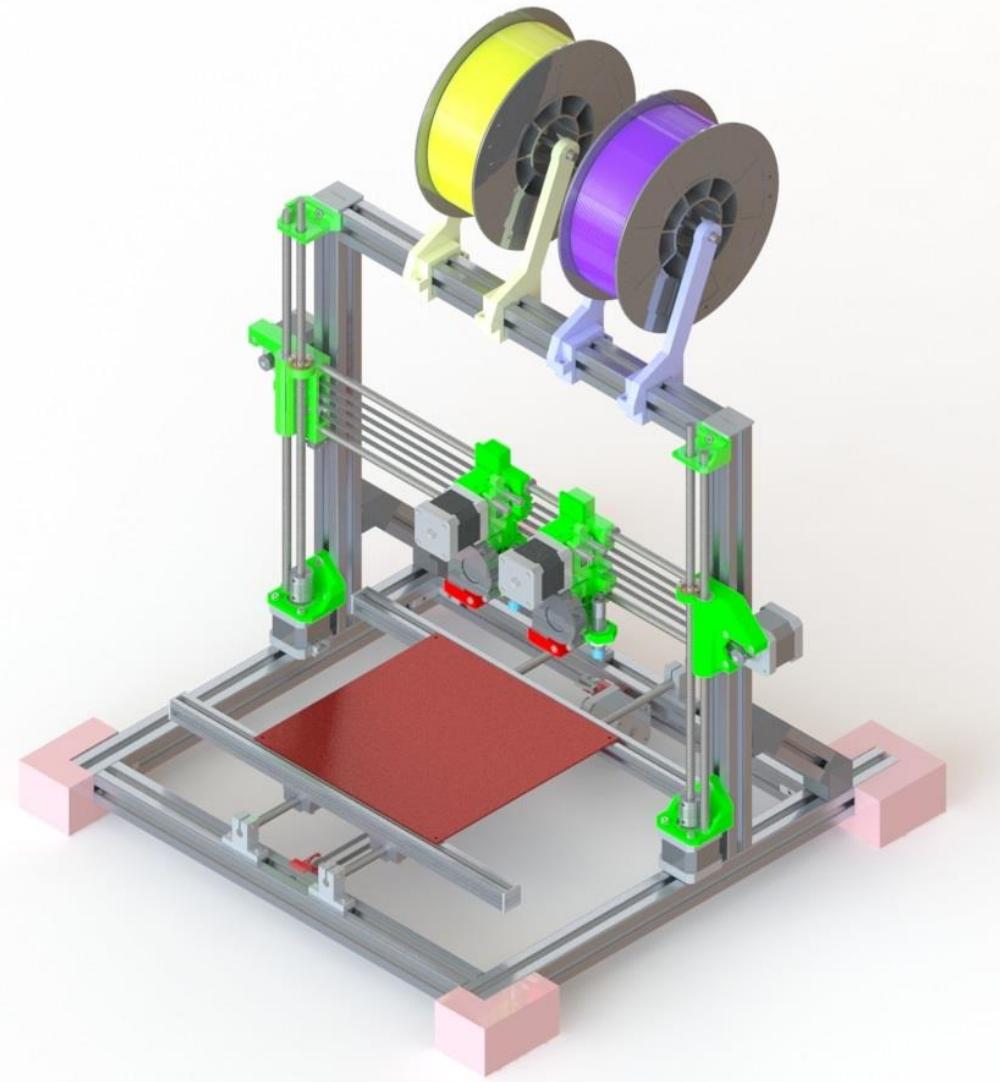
Ensamblaje impresora multmaterial de doble extrusor; Fuente: Elaboración propia con SW
